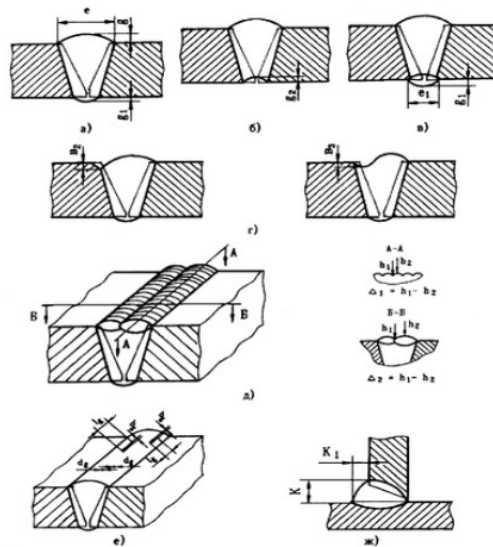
Размеры сварного шва, подлежащие измерительному контролю
